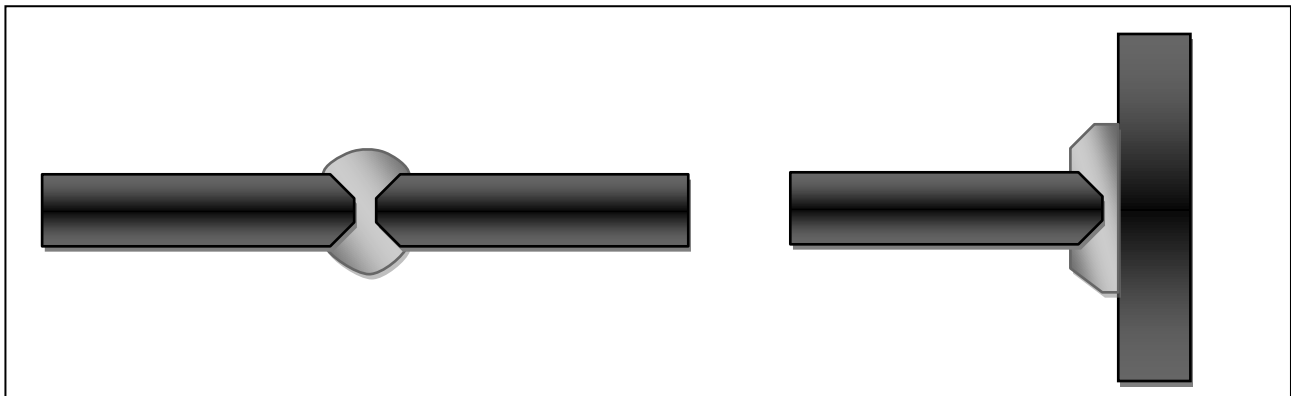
Assemblages soudés par joint en bout à pleine pénétration
